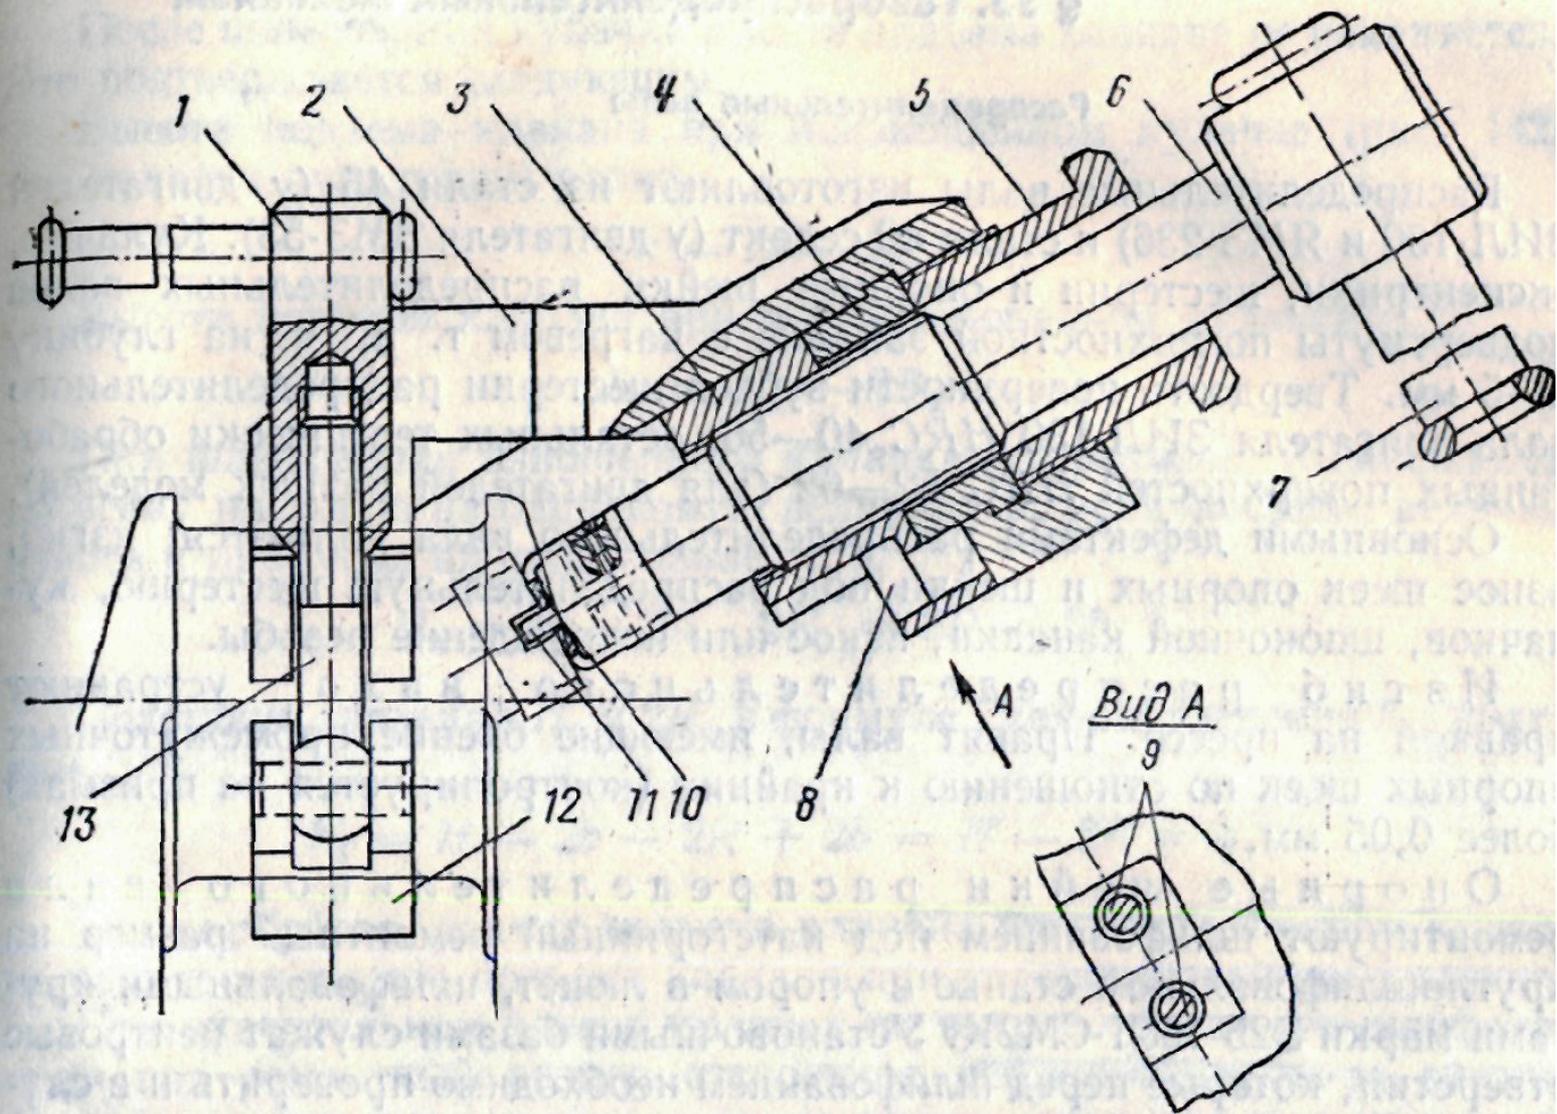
Отвертка для вывертывания пробок из коленчатого вала двигателя ЗИЛ-130:
